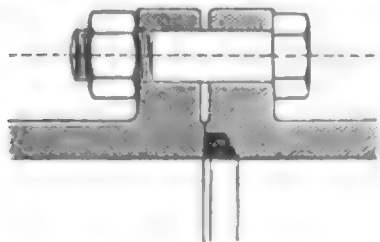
Kupferner Dichtungsring zur Flanschdichtung.
